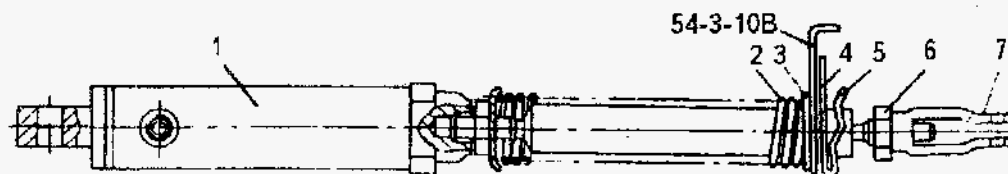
Гидроцилиндр привода механизма очистки сеток воздухозаборника:
